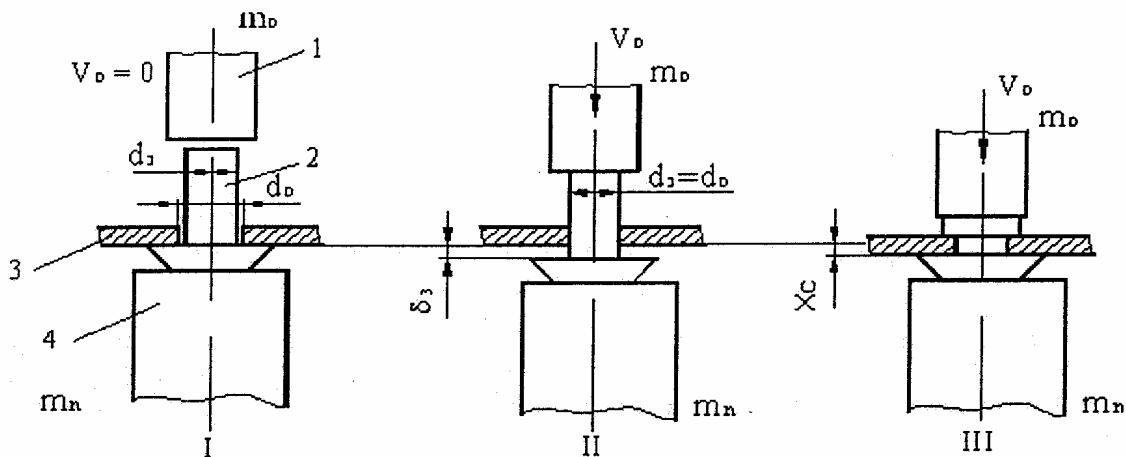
Механизм образования заклепочного соединения при импульсной клепке: 1 – обжимка; 2 – заклепка; 3 – пакет; 4 – поддержка
